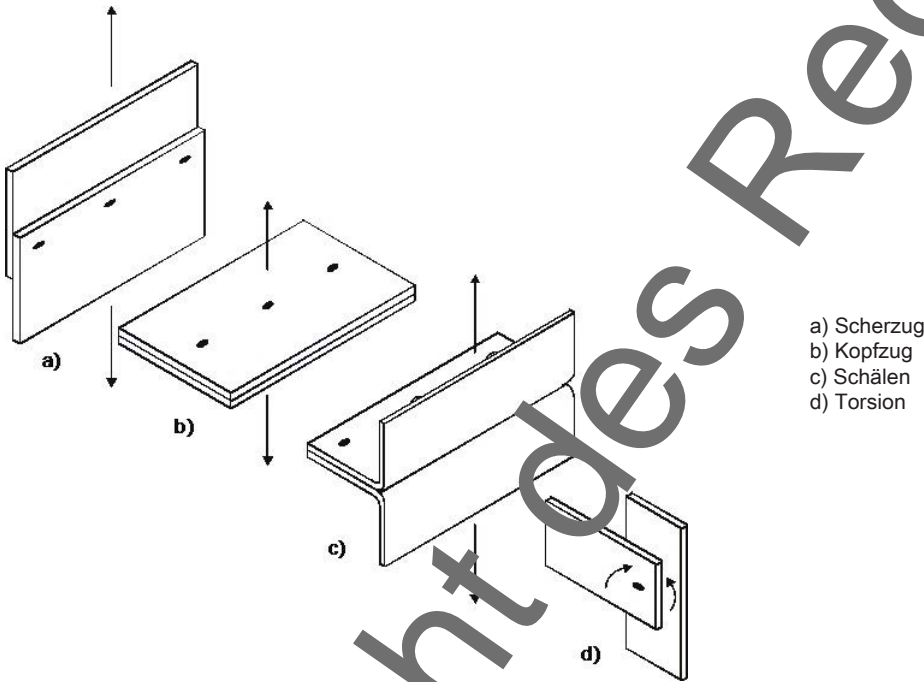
Reine Beanspruchungsarten einer Punktschweißverbindung.
